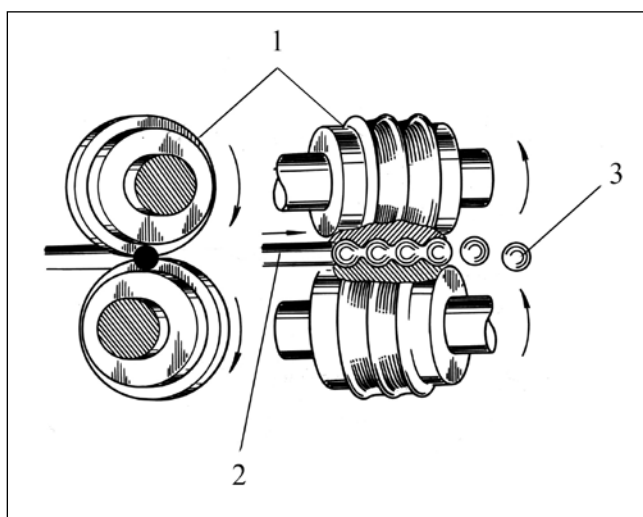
Прокатывание шаров на стане поперечно-винтового проката
